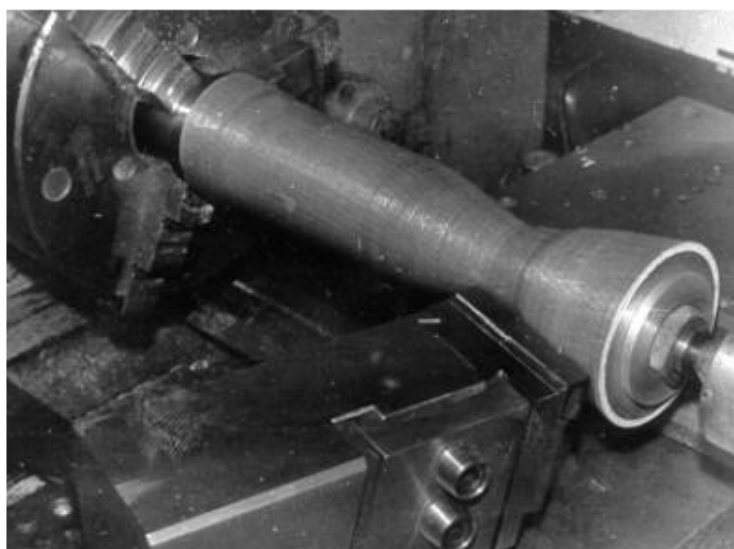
Вид заготовки корпуса двигателя из стеклопластика, установленной на токарном станке
